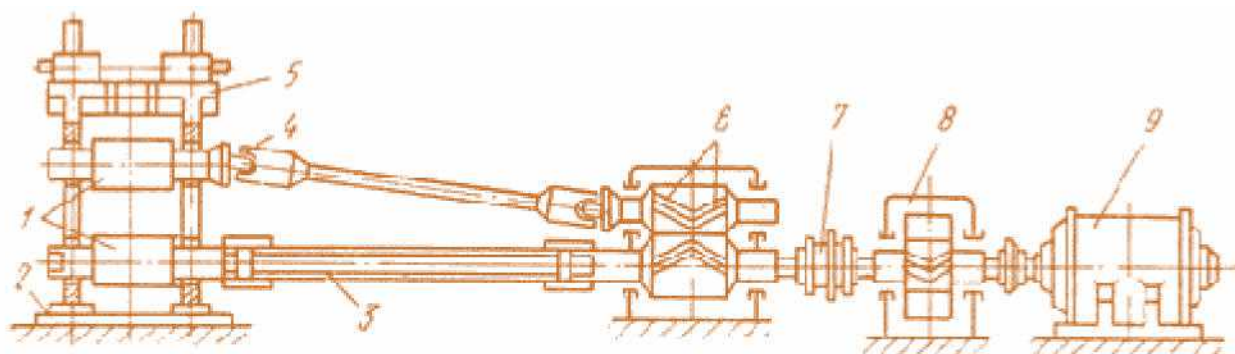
Схема головної лінії прокатного стану: 1-прокатні валки; 2-плита; 3-трєфовий шпиндель; 4-універсальний шпиндель; 5-робоча клітей; 6-шестеренна клітей; 7-муфта; 8-редуктор; 9-двигун.
